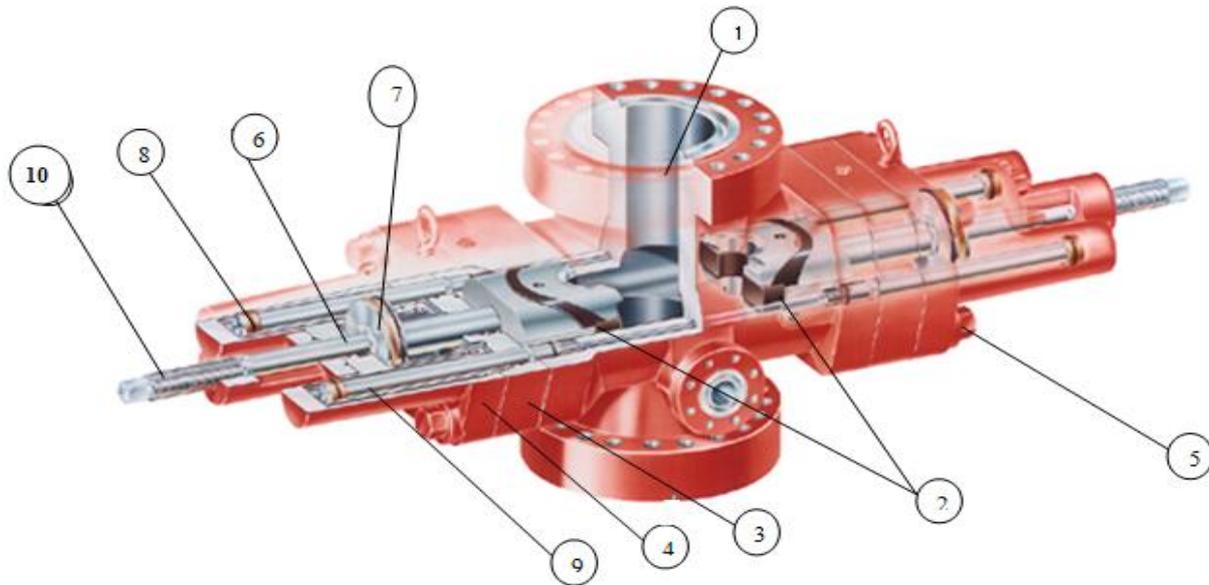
Obturateur Cameron type U équipé de pipes rams
